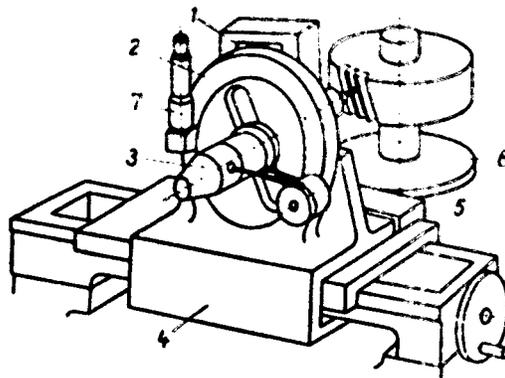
Flankenrichtungsprüfung längs der Schraubentite auf dem Zahnflanken-Prüfgerät von Klingelnberg
